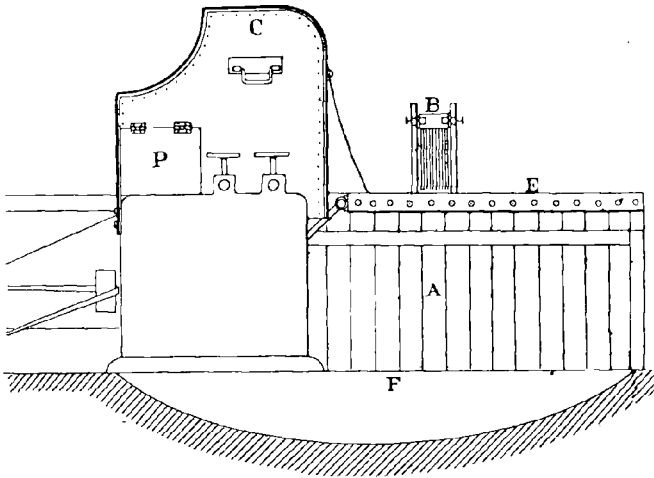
Captage de copeaux et poussières d'une parqueteuse.
